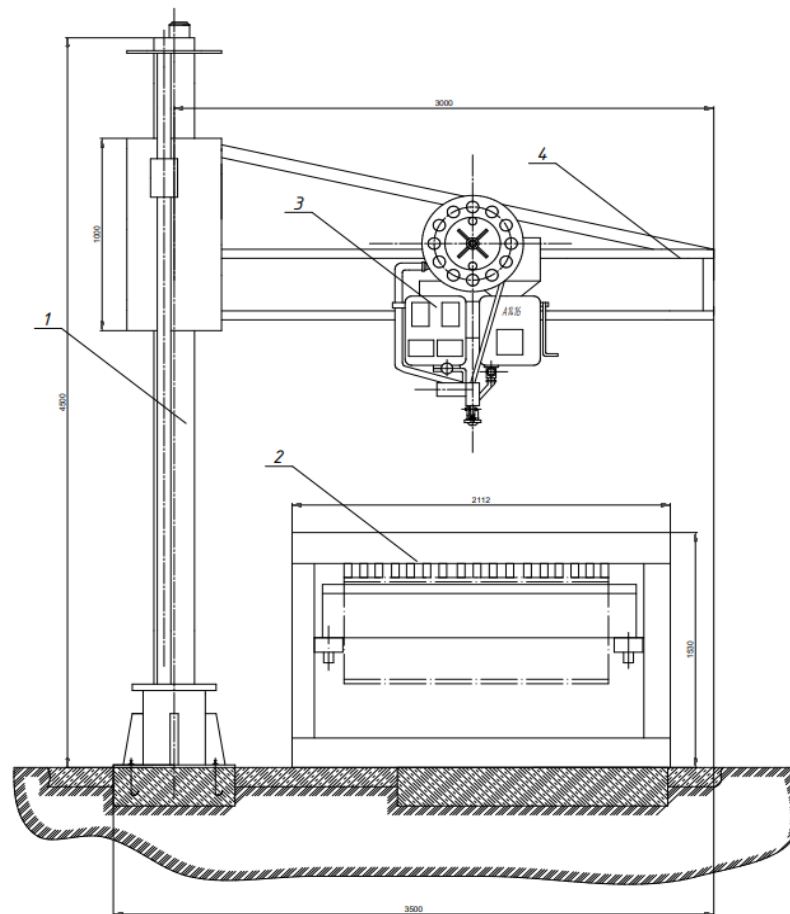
Стенд для зварювання поздовжнього стику обичайки:
